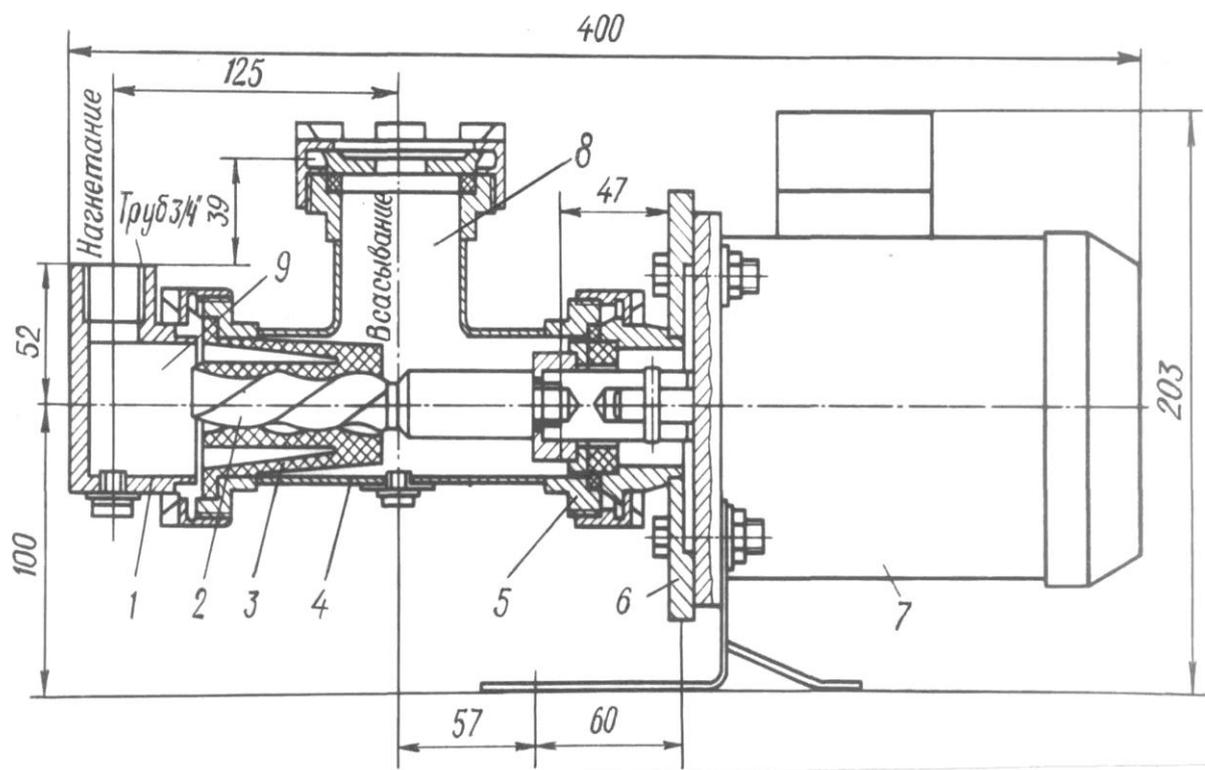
Общий вид одновинтового электронасосного агрегата марки П8-ОНВ: 1 – крышка; 2 – винт; 3 – статор (обойма); 4 – корпус насоса; 5 – фланец; 6 – основание; 7 – электродвигатель; 8 – всасывающий патрубок; 9 – нагнетательный патрубок
